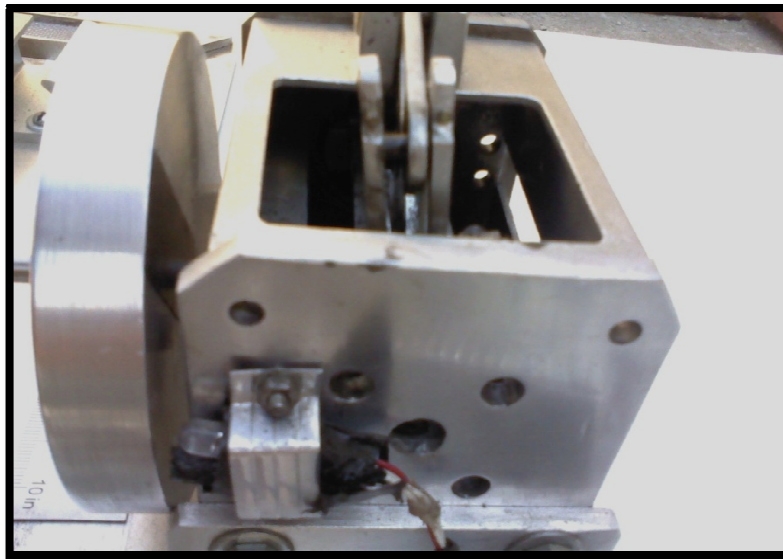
Sensor infrarrojo montado en la placa trasera del motor. Fuente: Elaboración propia
